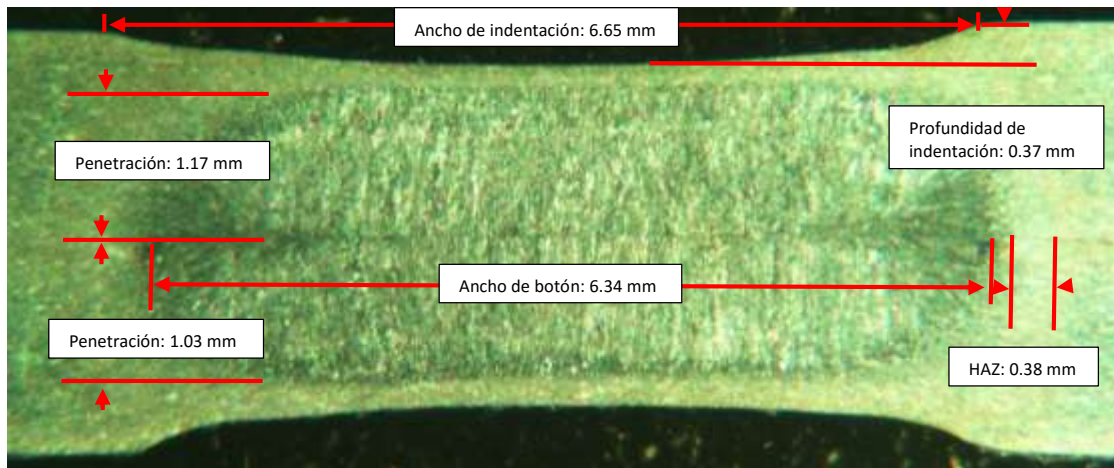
Mediciones realizadas en el botón de soldadura número 9.
